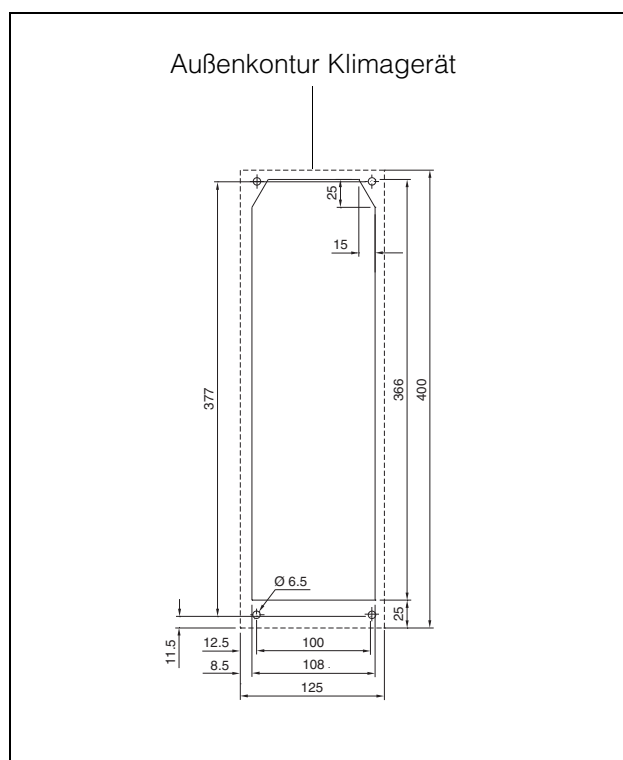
Montageausschnitt und Bohrungsmaße bei Geräteanbau
